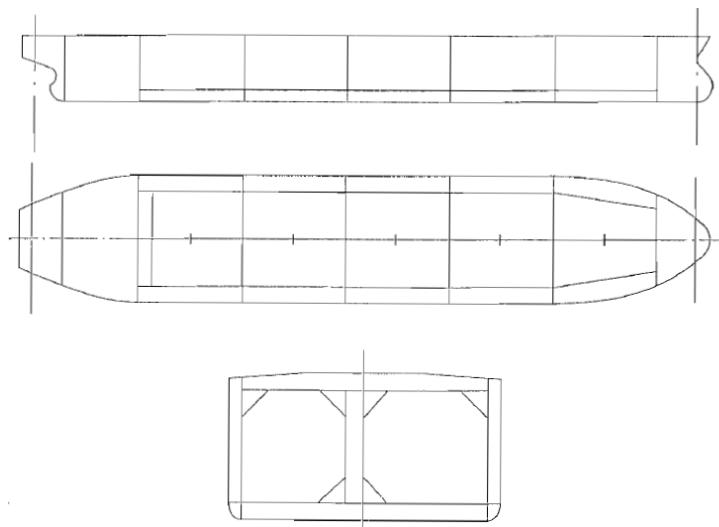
Esquema estructural de un petrolero con mamparo longitudinal
